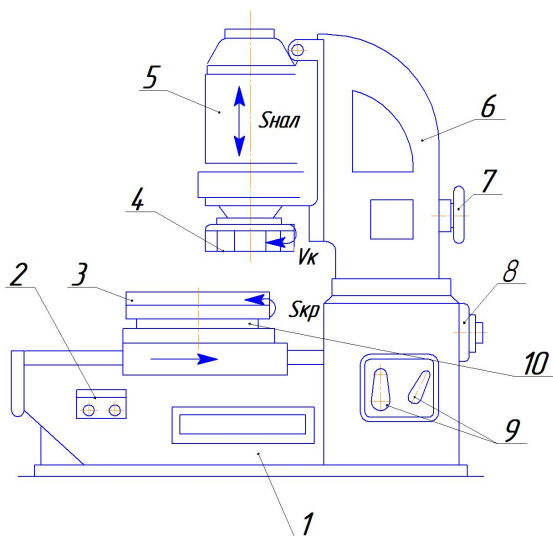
Плоскошлифовальный станок с круглым столом
